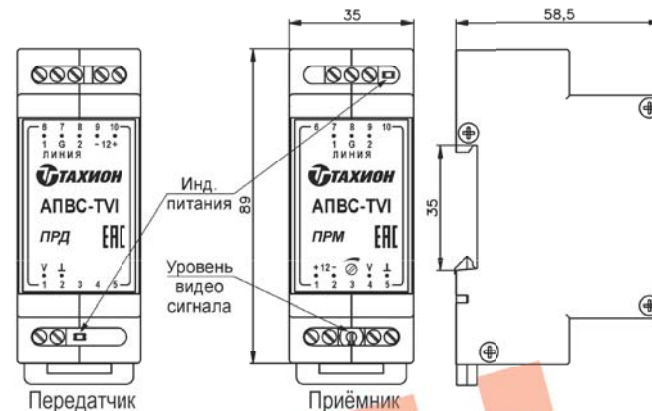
Устройство и габаритные размеры АПВС-ТВИ
